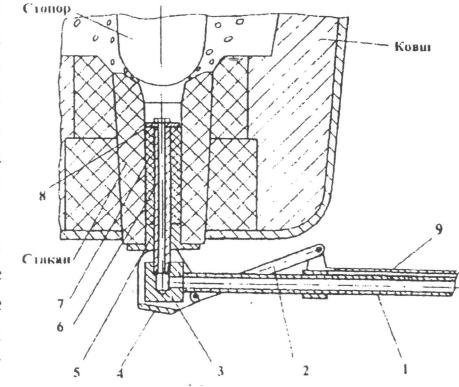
Схема устройства для продувки стали газом в стопорном разливочном ковше.
